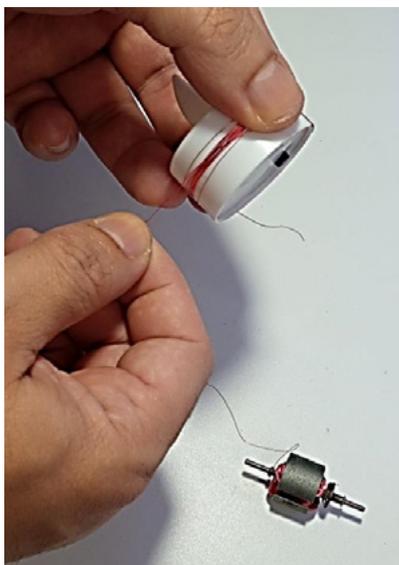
Enrolando nossa bobina usando um molde (qualquer objeto circular).
